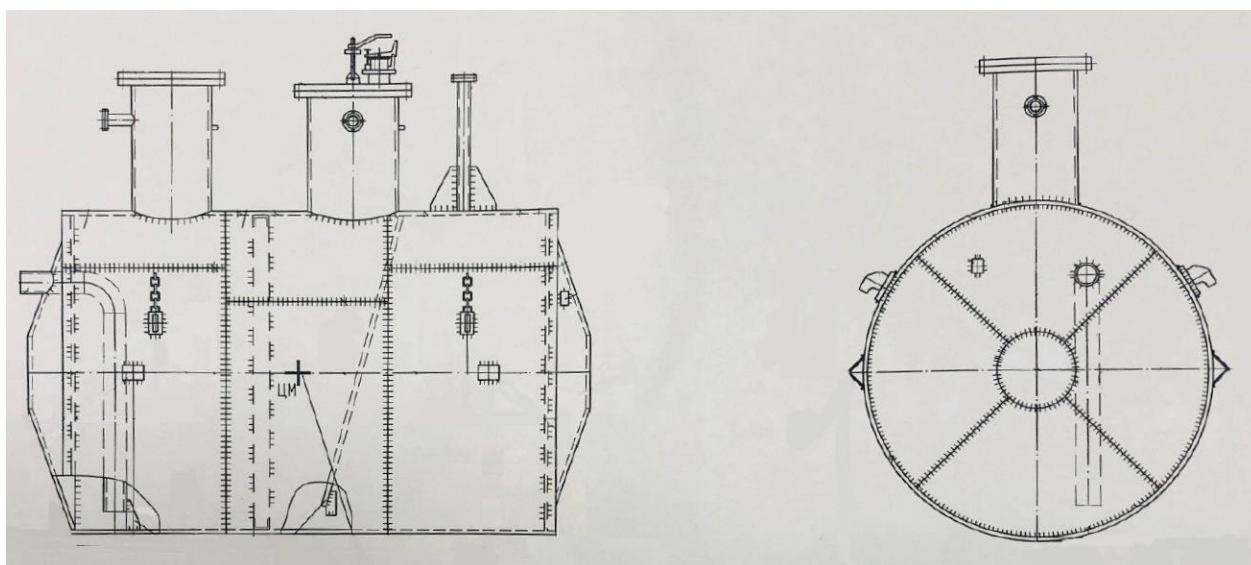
Общий вид эскиза резервуаров РГС-20
